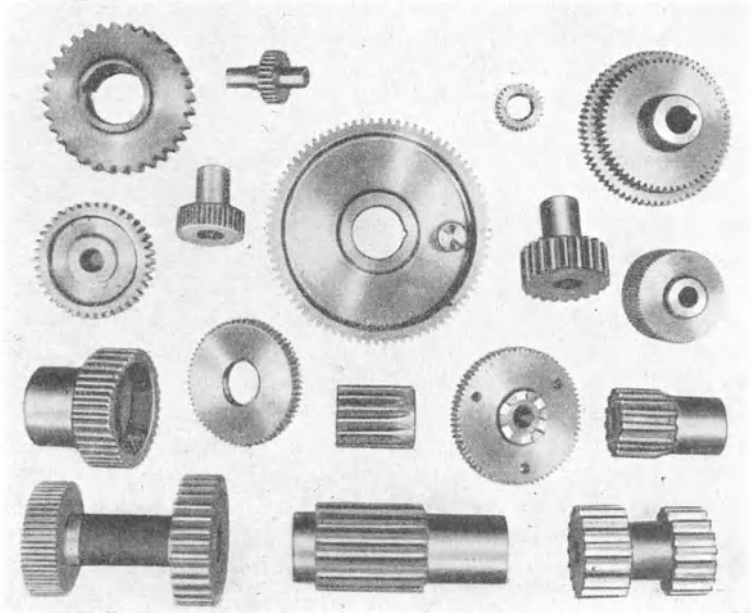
Verschiedene Ausführungsformen von Radkörpern bei Werkzeugmaschinen.
